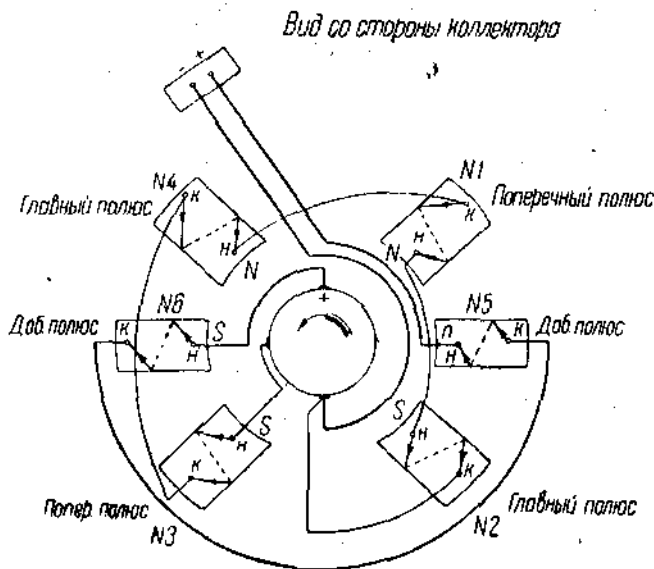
Схема сварочного генератора завода «Электрик» СМГ-1.
